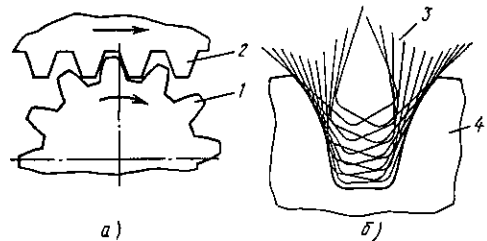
Зубофрезерование цилиндрических колес: а – зацепление червячной фрезы с колесом; б – образование эвольвентного профиля
